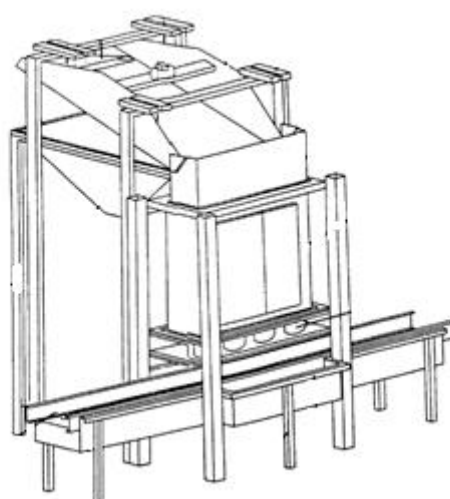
Máquina automática de llenado de moldes para la fabricación de quesos.
